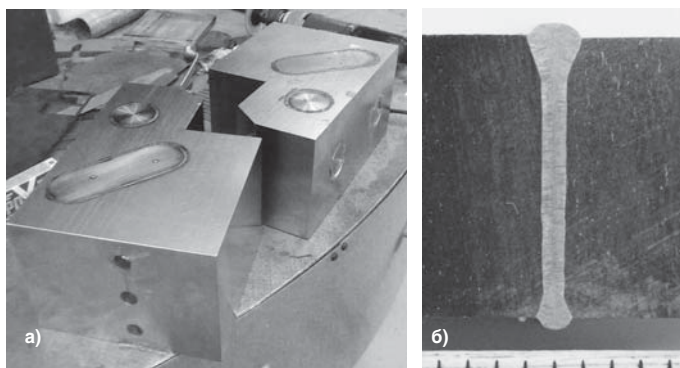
Коллекторы внешней отражающей мишени ЦСД из стали XM-19: а) после лазерной сварки б) макрошлиф сварного шва толщиной 10 мм
